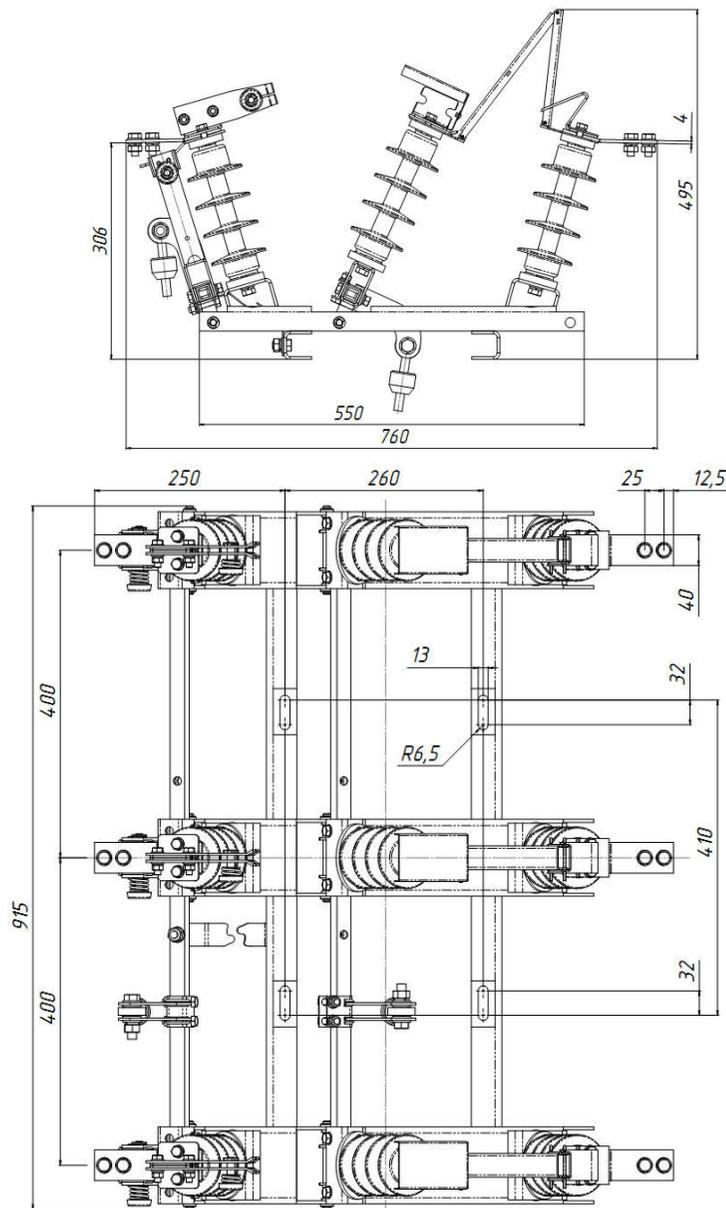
Б Разъединитель РЛК-1а-II-10/400 –УХЛ1
